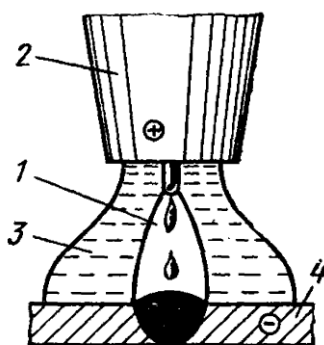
Схема автоматической сварки под флюсом
